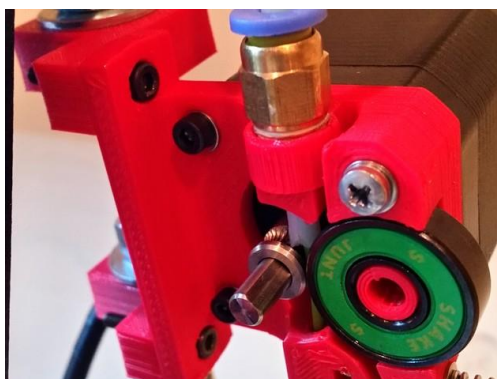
Model tlačiacej hlavy Diamond Hot End.
